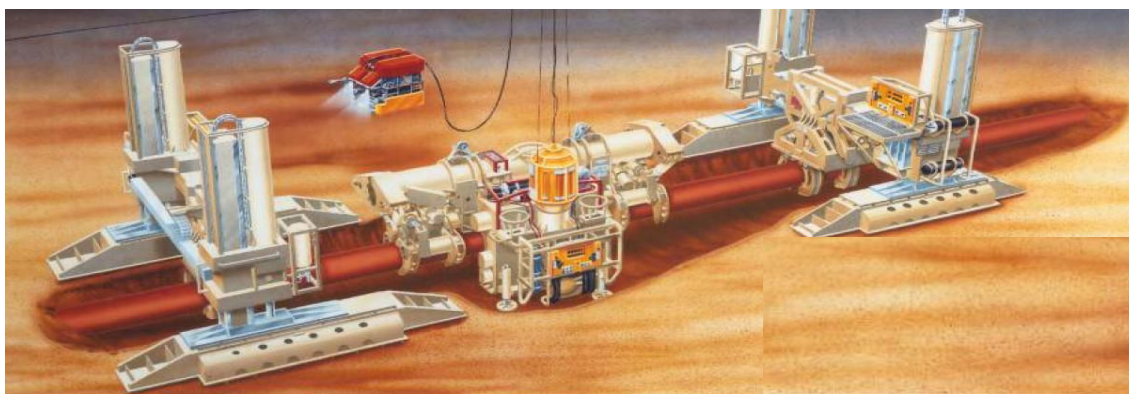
Образец подводной сварочной камеры
